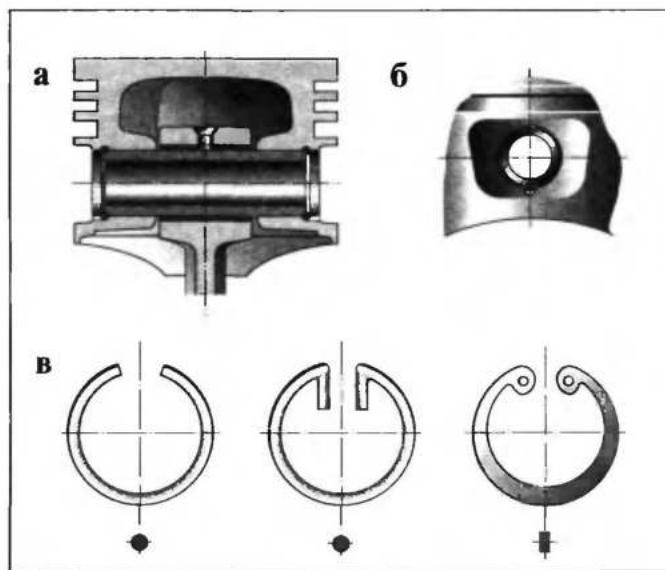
Фиксация поршневого пальца от осевого перемещения: а — схема; б — паз для демонтажа кольца; в — основные типы колец
